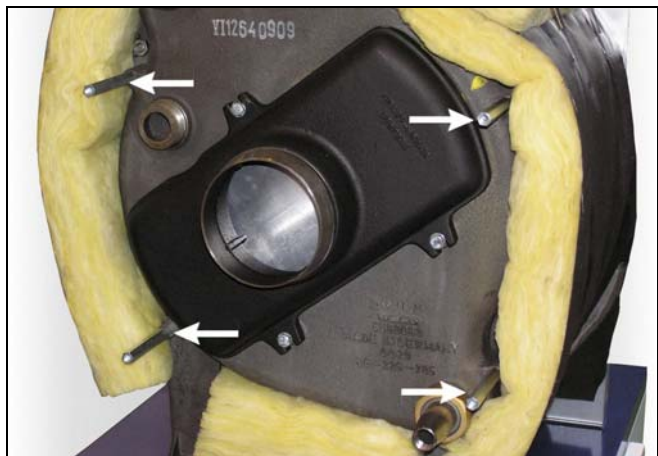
Schrauben Sie die vier Distanzstücke mit dem kurzen Gewinde auf der Rückseite des Kessels ein.
